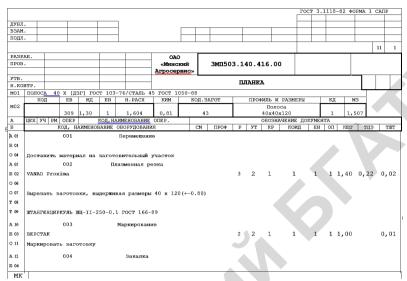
Фрагмент маршрутной карты изготовления детали Планка
